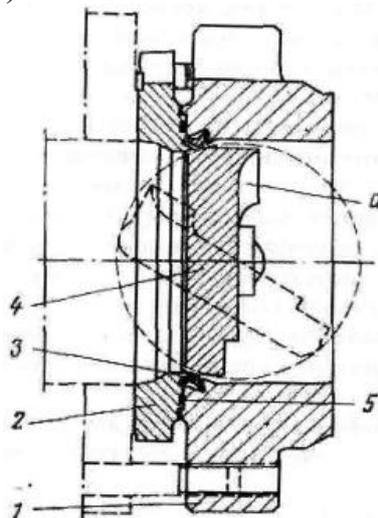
Дисковый затвор с эластичным уплотнительным кольцом в корпусе:
